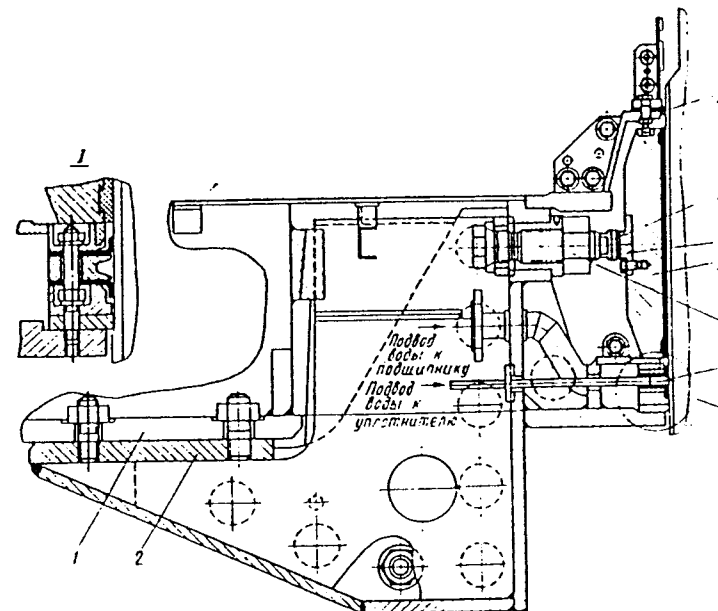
Направляющий подшипник с водяной смазкой:
